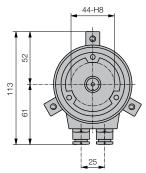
Grundgerät zum Anbau an Messgeräte mit drehbarer Zeigerwelle. Das Messgerät muss mit rückseitig verlängerter Zeigerwelle (Durchmesser 1,5 mm, Länge 6...7 mm) ausgeführt werden.
